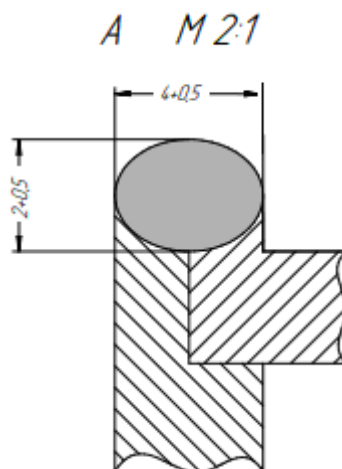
Внешний вид сварного шва крышки с защитным корпусом
